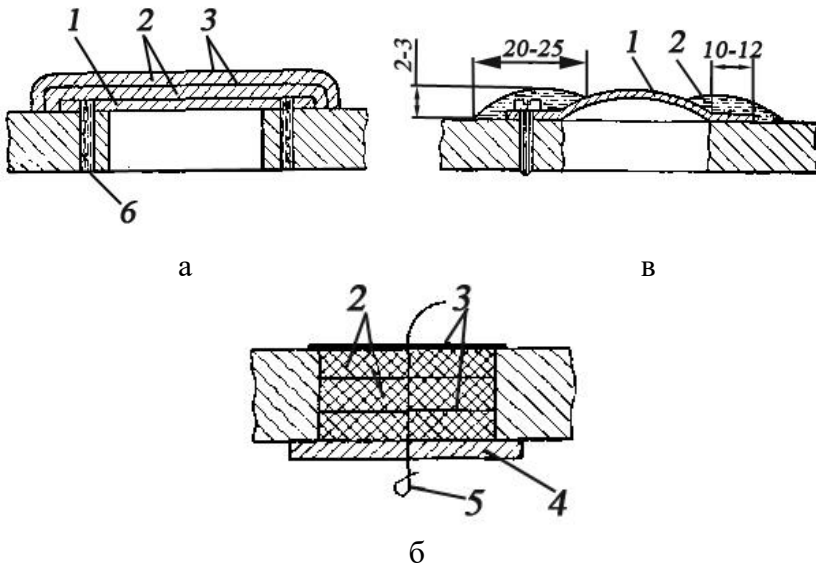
Зароблювання пробоїн у деталях епоксидною композицією: а — внапусток; б — врівень (деталі тонкостінні); в — накладанням металевої накладки на гвинтах; 1 — металева накладка; 2 — епоксидна композиція; 3 — тканинна накладка; 4 — підтримуюча металева пластина; 5 — дріт; 6 — штифт.
